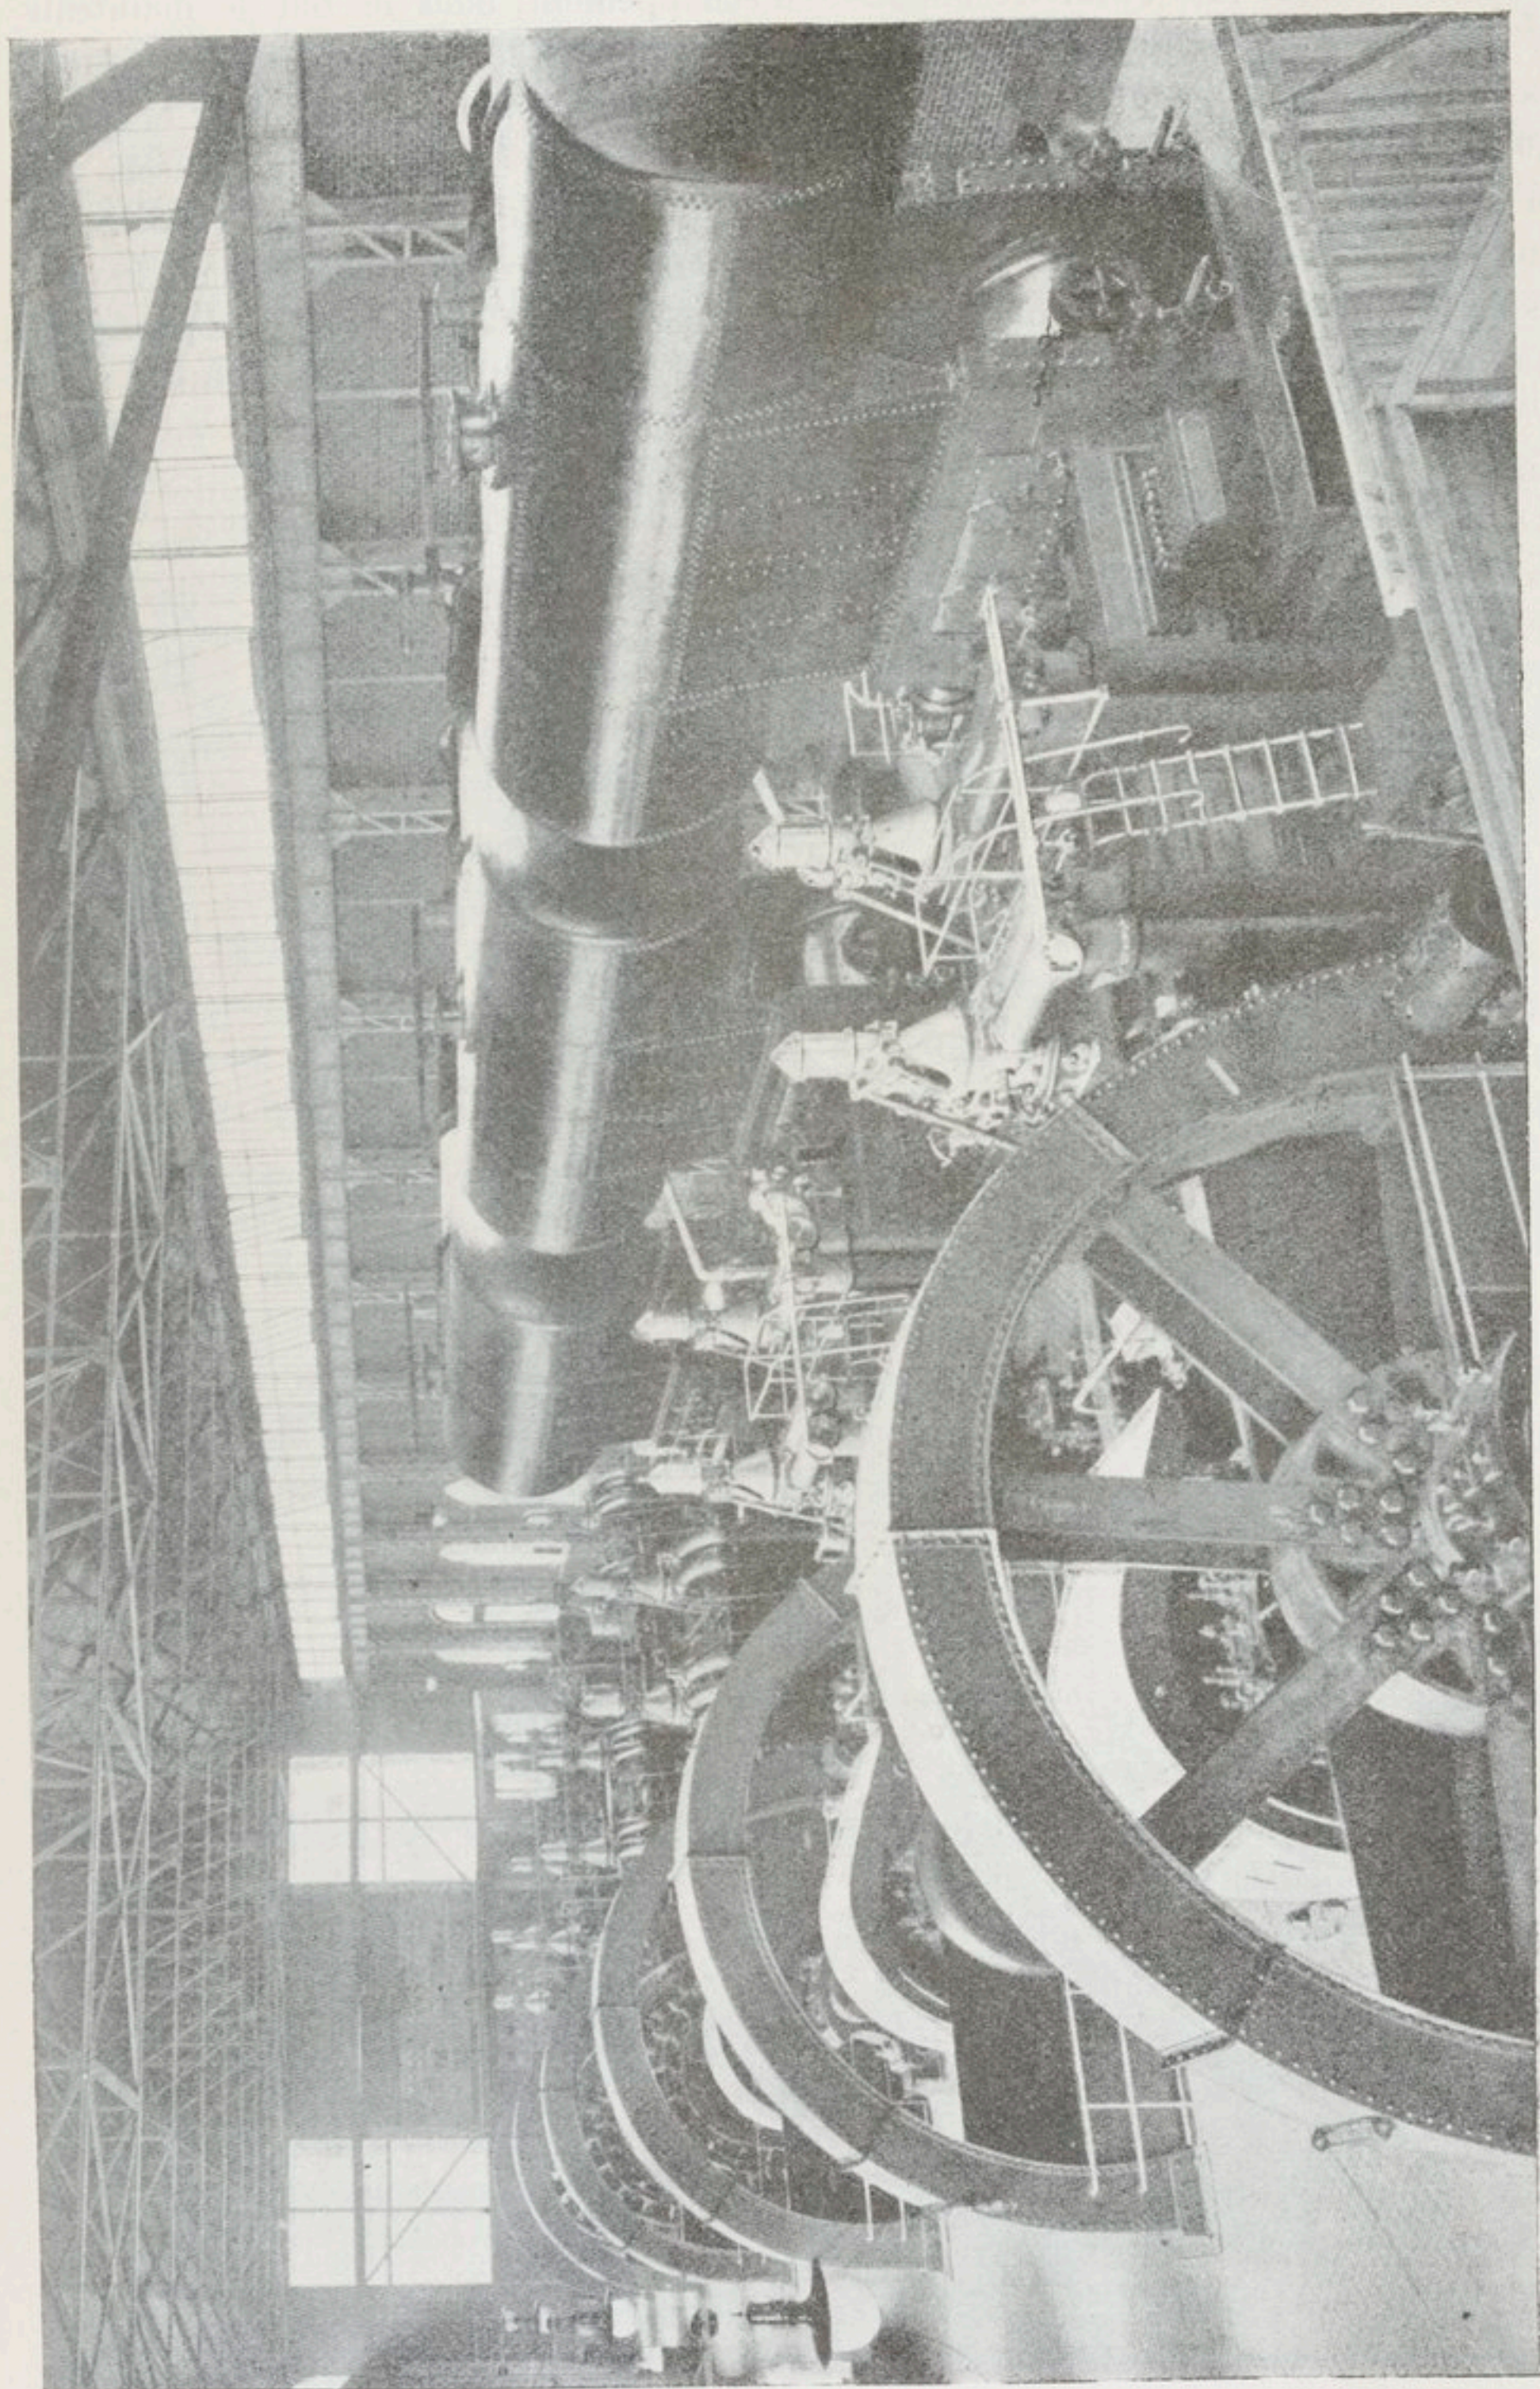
Trois machines soufflantes à gaz Cockerill de 600 chevaux, et trois moteurs à gaz Cockerill de 1.400 chevaux chacun.
